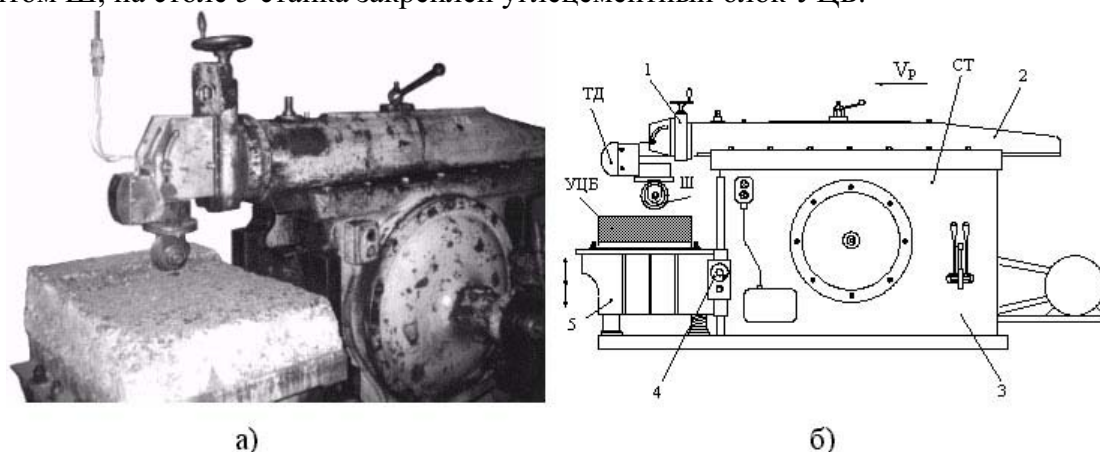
Вид (а) и схема (б) стенда для исследования процесса резания материала режущим инструментом с вращающейся режущей частью: СТ — станок; Ш — режущий инструмент; ТД — тензометрический динамометр; УЦБ — углицементный блок; 1 — суппорт; 2 — ползун; 3 — корпус станка; 4 — рукоятки вертикального и горизонтального перемещения стола; 5 — стол
